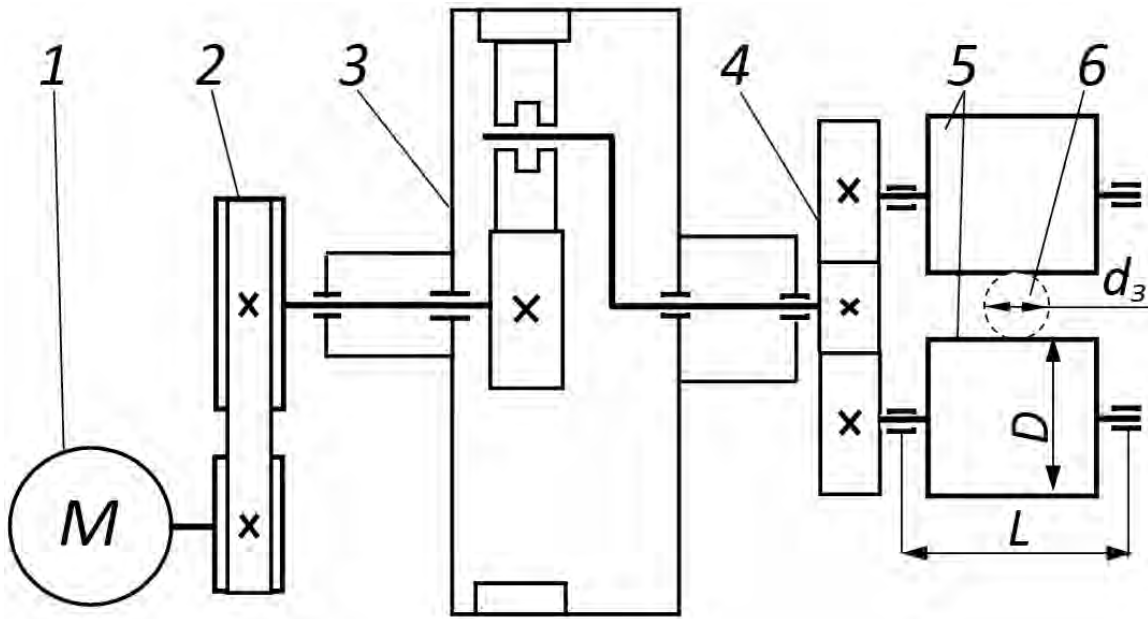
Схема привода для профилирования заготовок (вид сверху): 1 – асинхронный электродвигатель; 2 – ременная передача; 3 – планетарный редуктор; 4 – открытая зубчатая цилиндрическая передача с разделенным потоком мощности; 5 – приводные валы с профилирующими валками; 6 – заготовка
